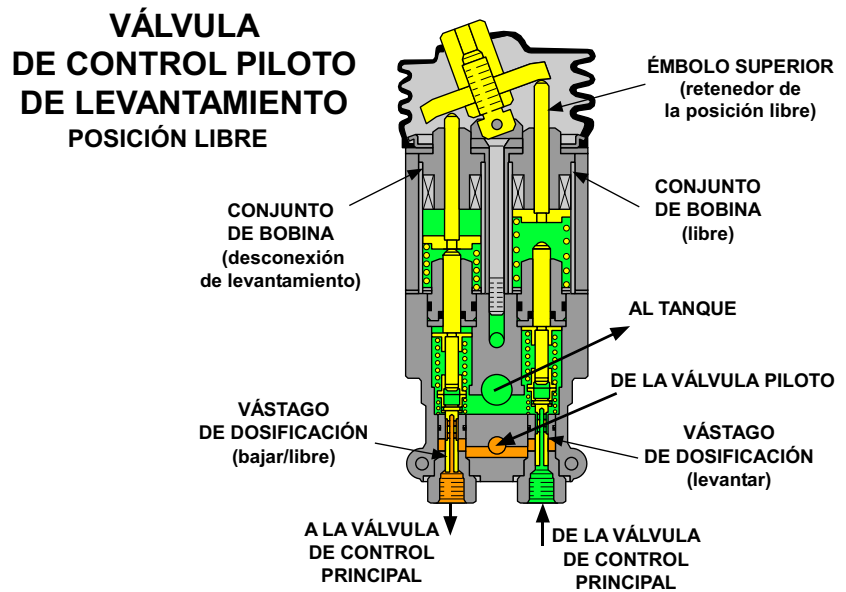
Válvula de control piloto de levantamiento (POSICIÓN LIBRE)
